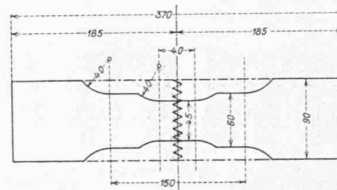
Zerreißprobestab mit Schweissnaht quer zur Stabaxe.
